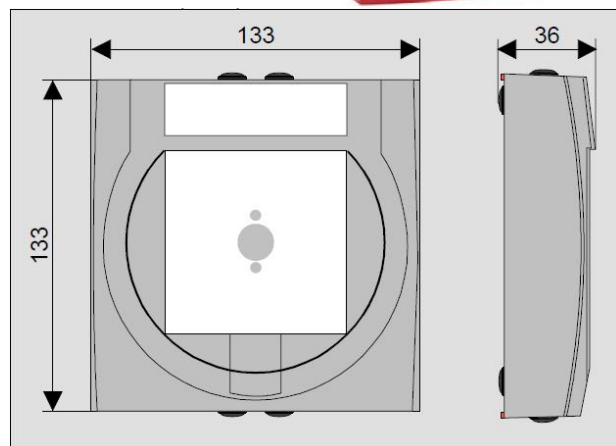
Ручной извещатель в большом корпусе (в сборе)
